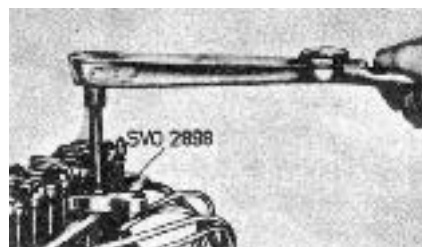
SVO 2898 Nyckel 11/16" för efterdragning av cylinderlocksskruvar
